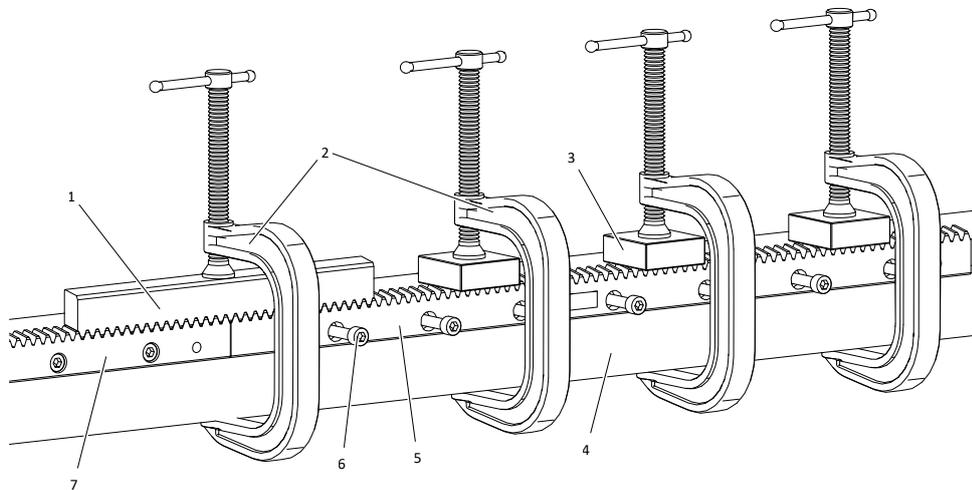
Montage einer weiteren Zahnstange (Beispiel)
